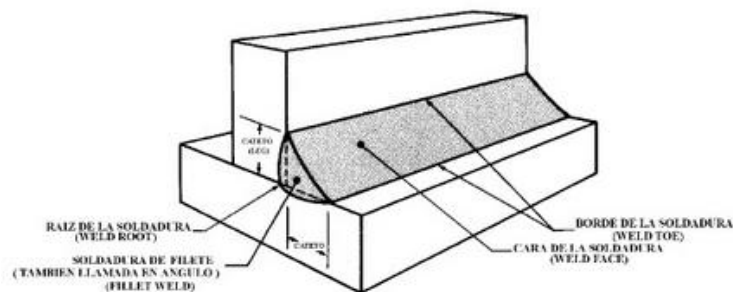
“Soldadura de filete”. (Instituto de ensayo de materiales)
